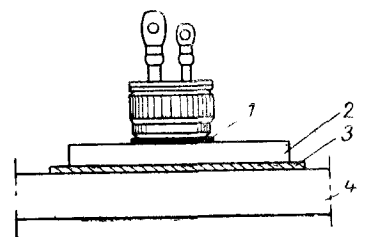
Монтаж вентиля на промежуточной пластине, изолированной от теплоотвода.
